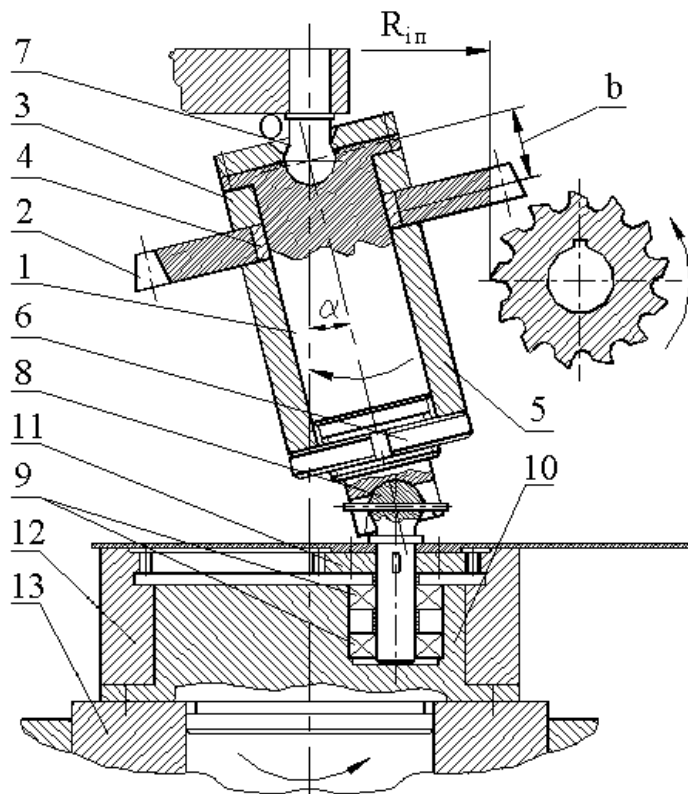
Приспособление для обработки зубьев сателлита прецессионной передачи
